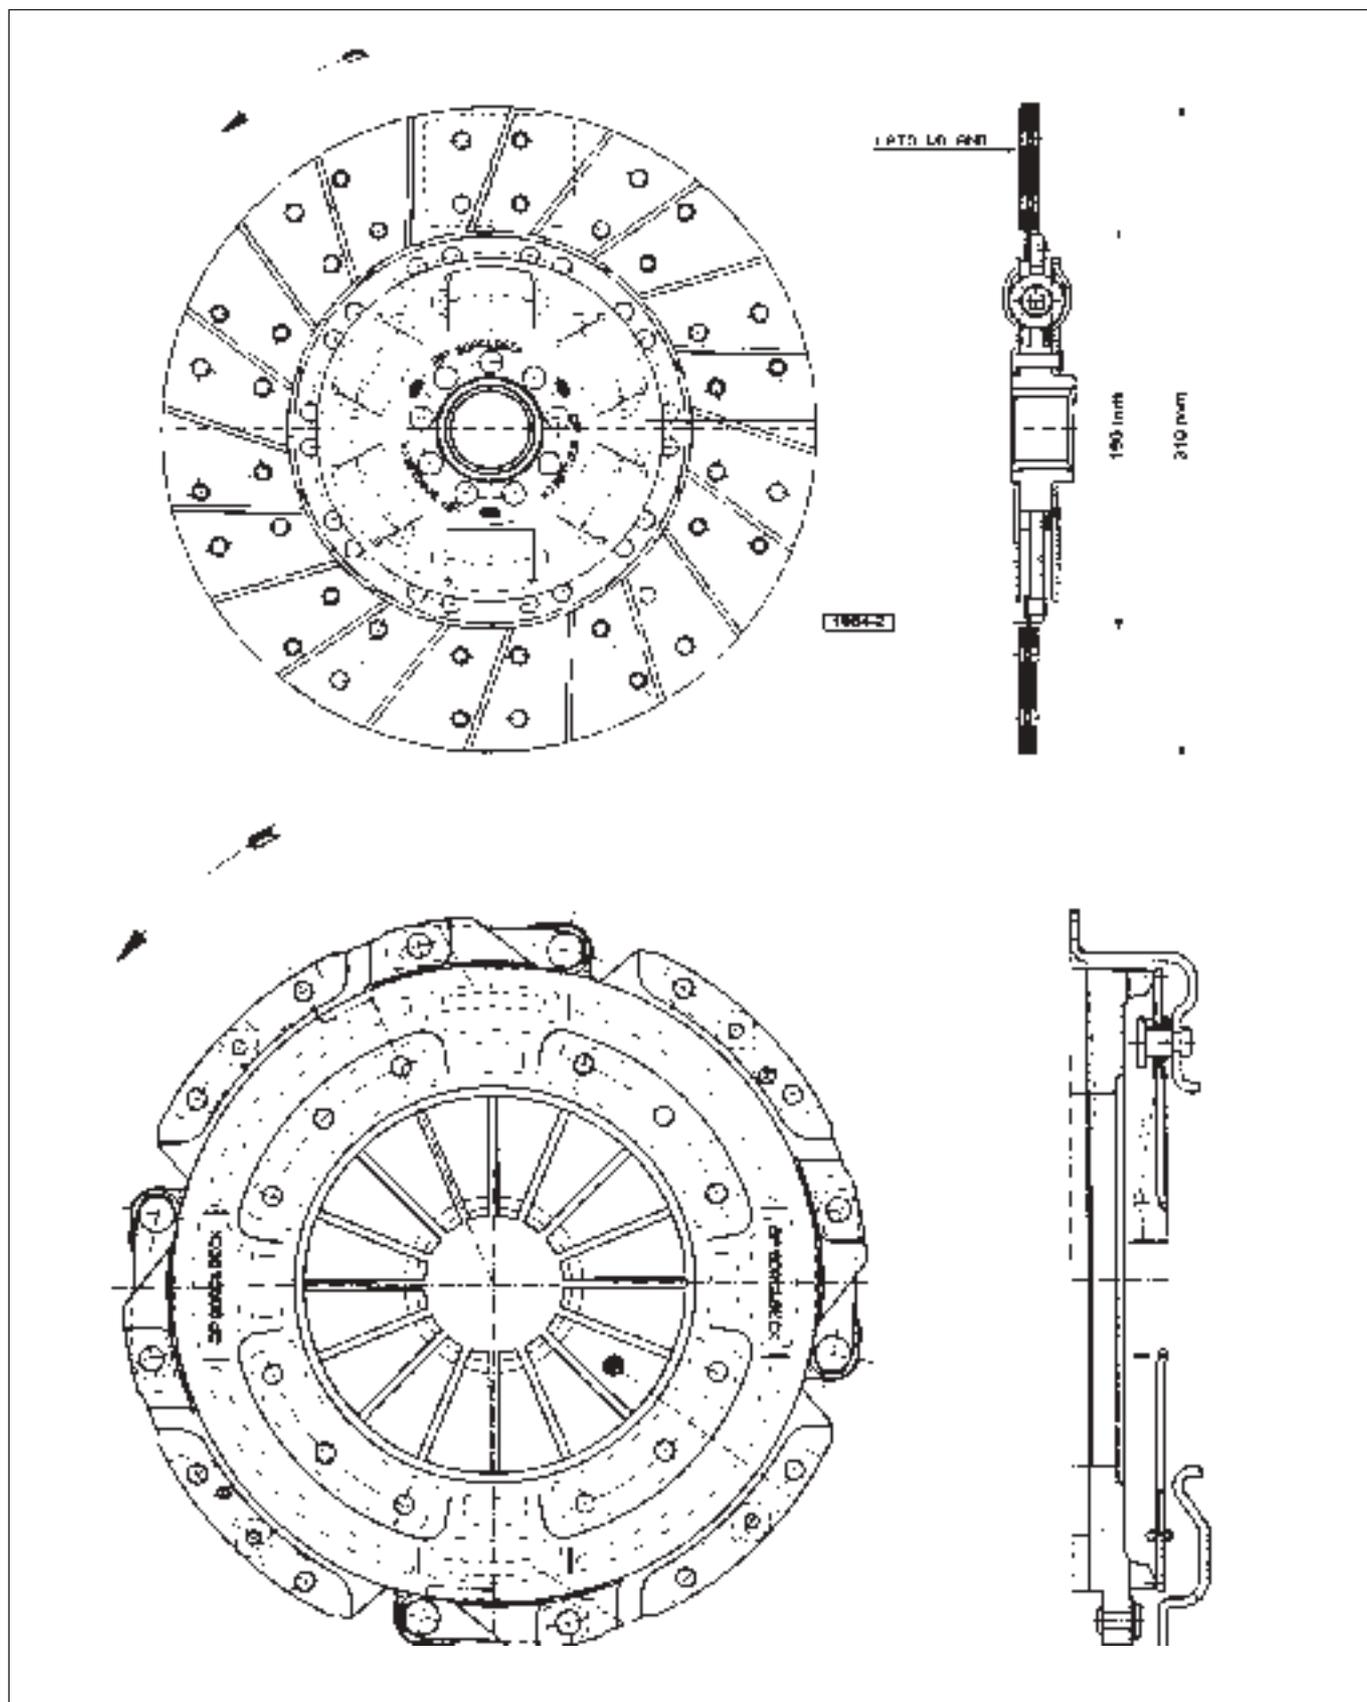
Vue d'ensemble de l'embrayage pour AGROPLUS 70 - 80
